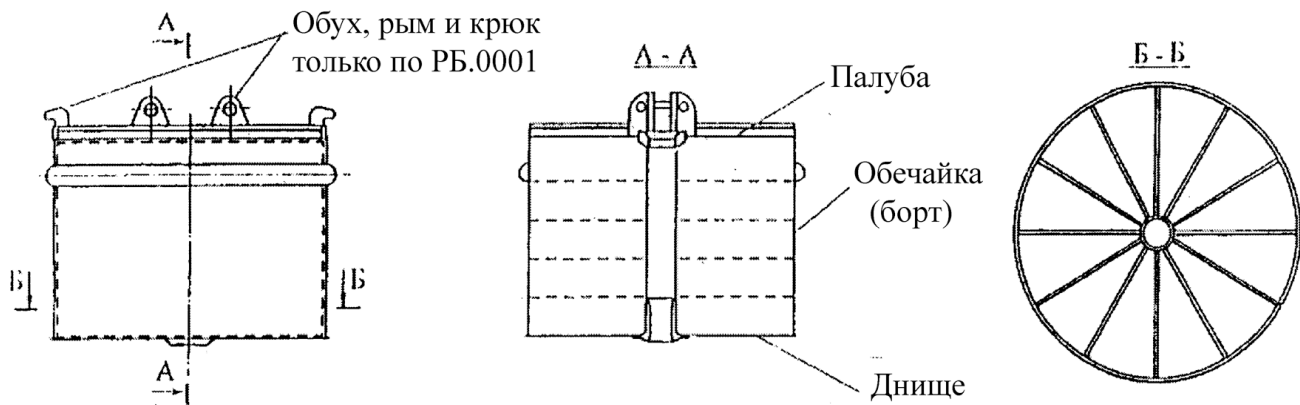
Конструкция корпуса рейдовой бочки
